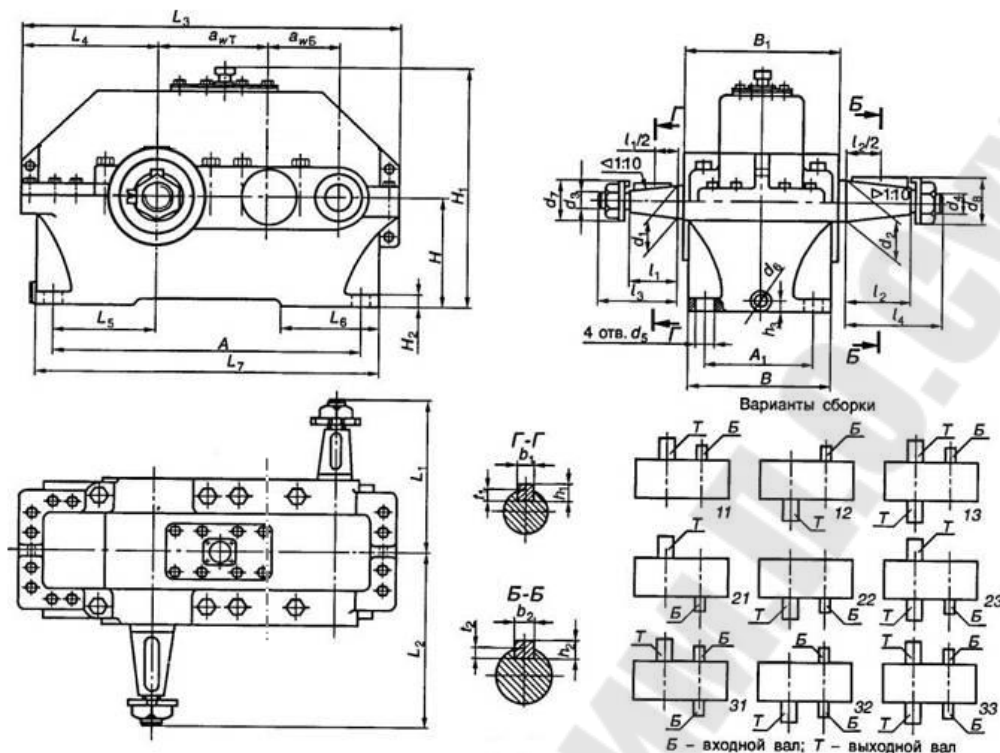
Габаритные и присоединительные размеры цилиндрических двухступенчатых редукторов типа 1Ц2У
